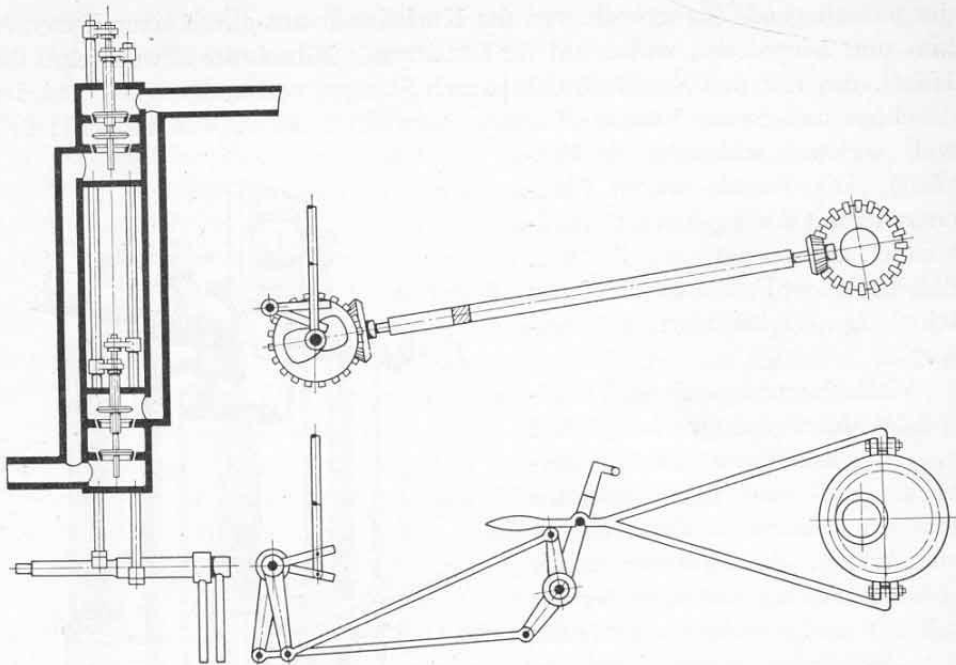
bis 277. Ventilsteuerungen um 1810.
